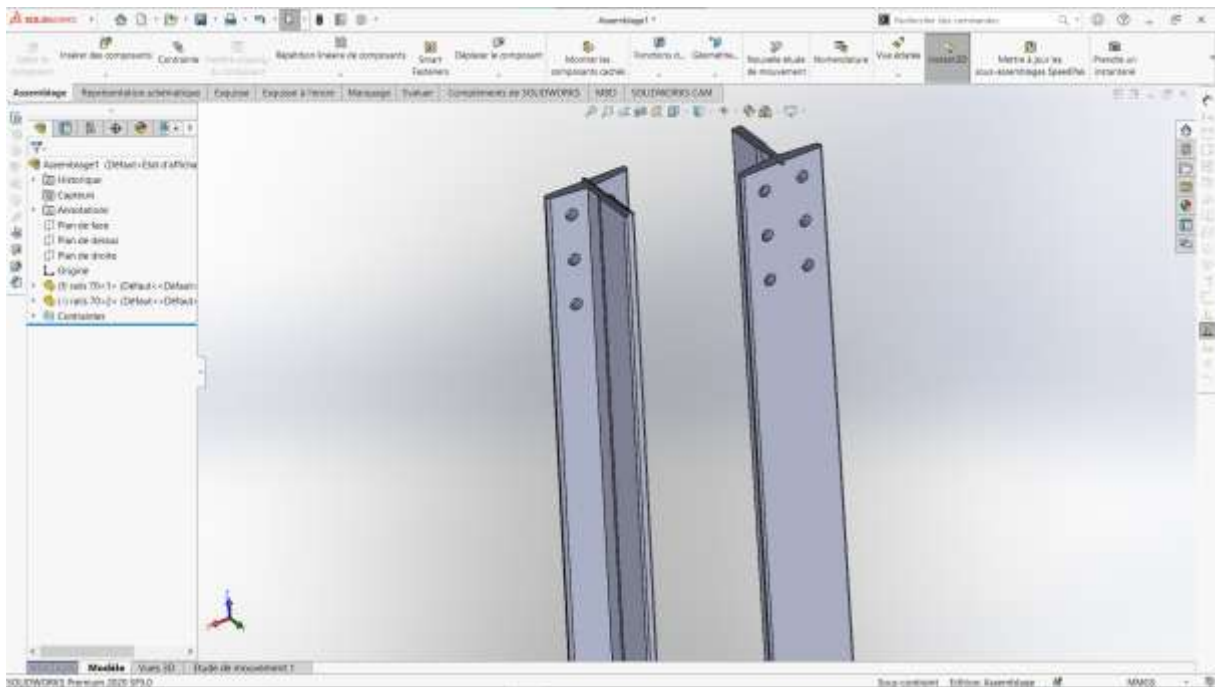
Conception d'une poutre IPE300 personnalisée
